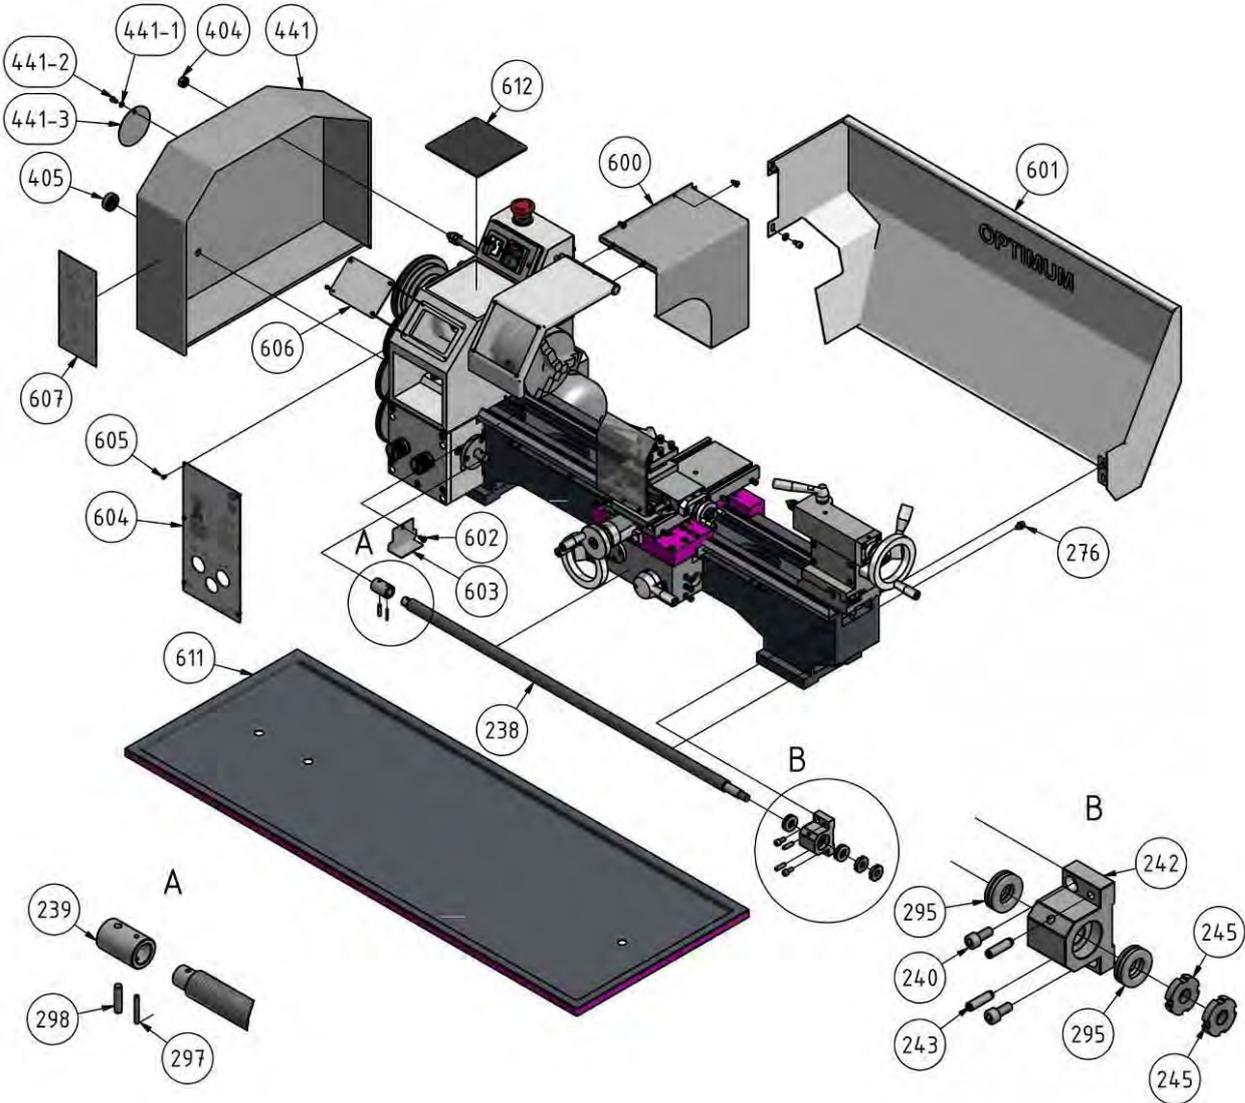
Maschinenbett - Bancada de máquina TU 2506
